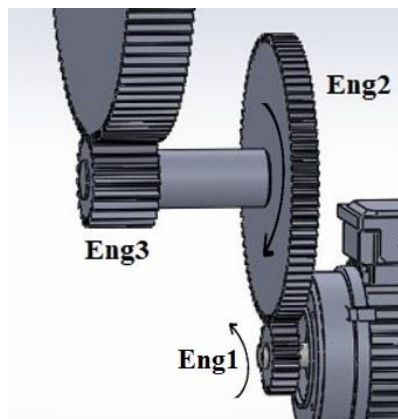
Sentidos de rotação do motor e engrenagens do eixo 1. Fonte: Autores.
